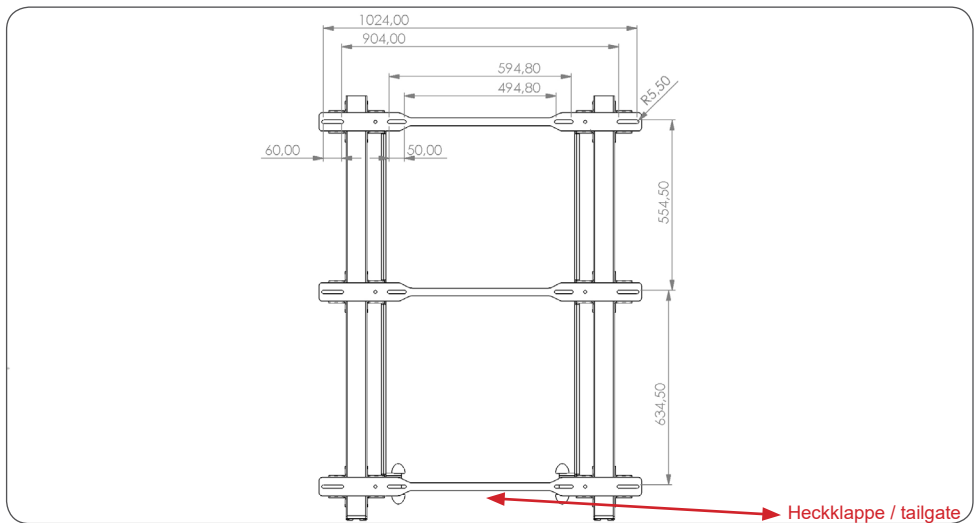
Bohrungen für Verankerungen im Ladebett / mouning hole positions on the cargoslide
